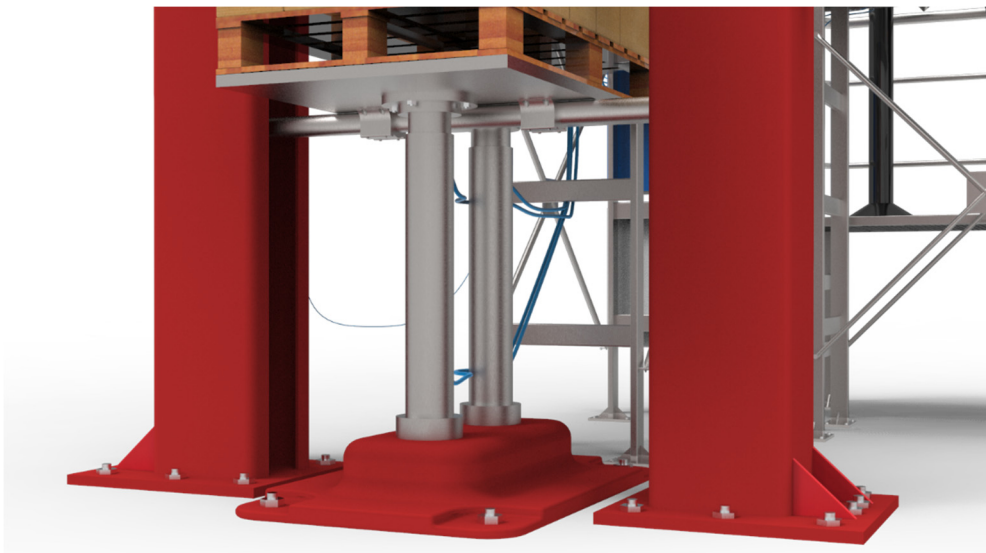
Cilindros elevadores (F y G), plataforma elevadora y columnas guía
